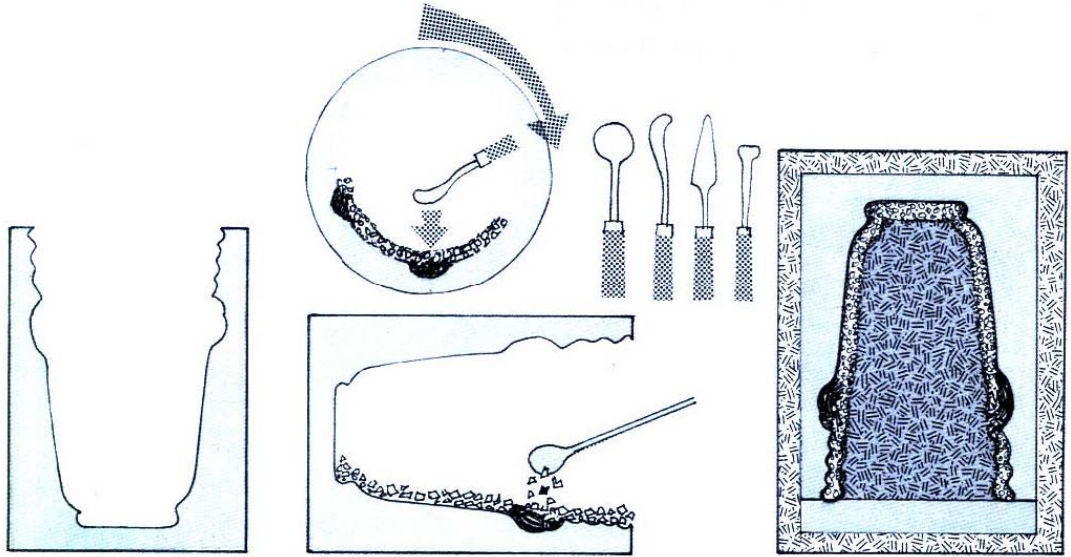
Fırın döküm Tekniği ile üretilmiş cam objeler
